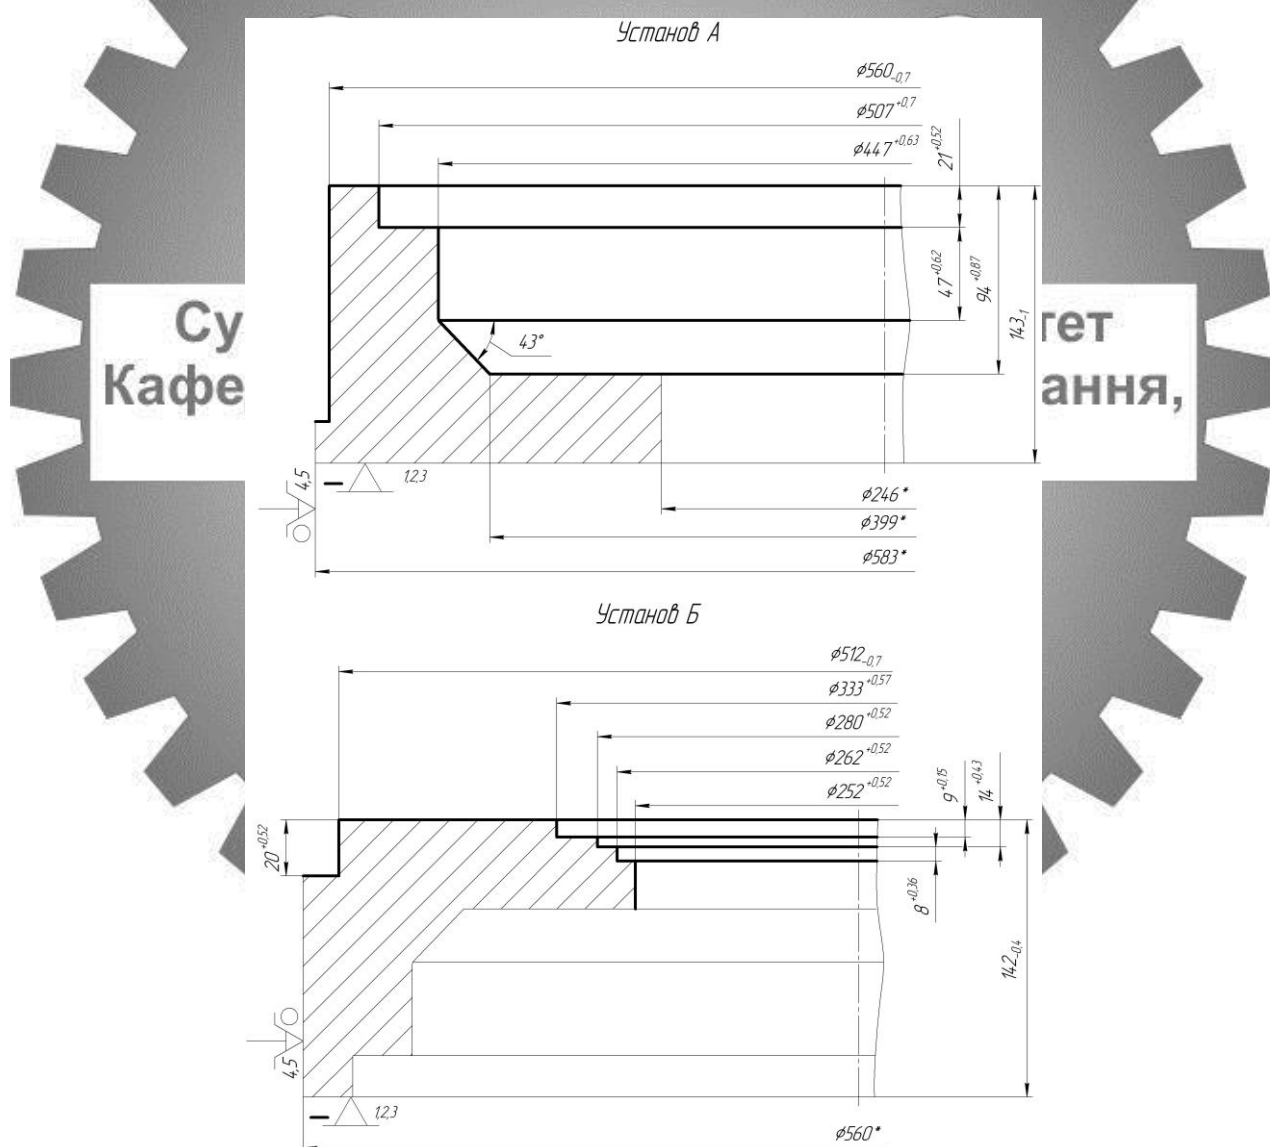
Схема базування заготовки на токарній операції (другий варіант)
